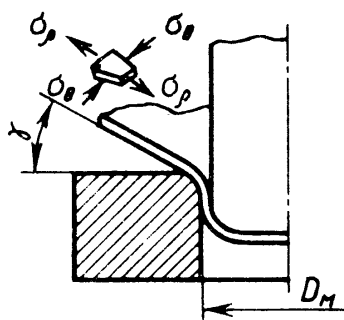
Начальный момент вытяжки без прижима заготовки
